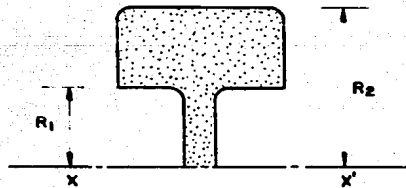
SECCION TIPO DE UN VOLANTE DE INERCIA
